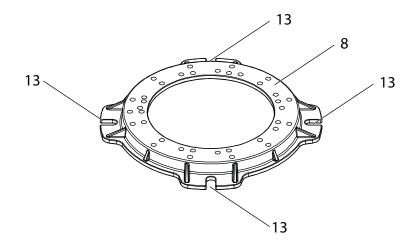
Mechanische Demontage – Befestigungsfuß – Beispiel
